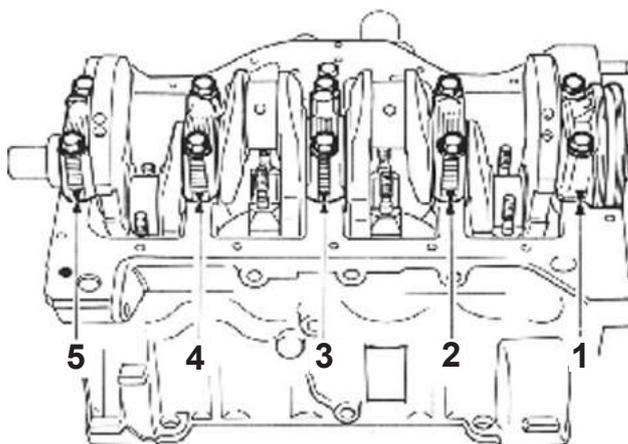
Cambota com 5 (cinco) apoios montada sobre o cárter superior do bloco
